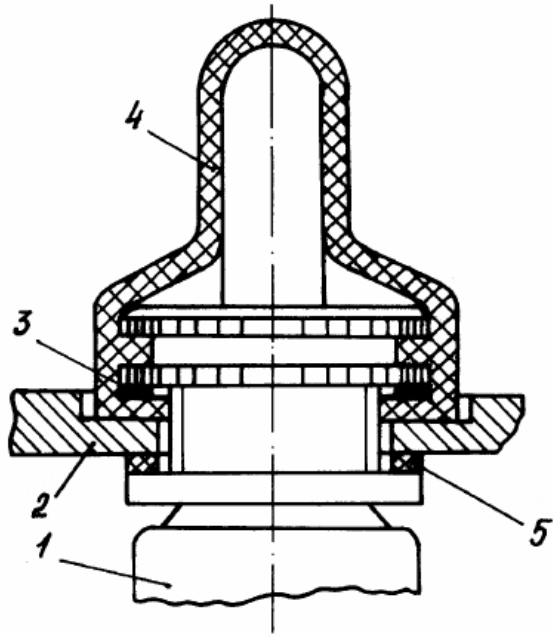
Ущільнення рукоятки тумблера за допомогою гумового ковпачка: 1 – тумблер; 2 – лицьова панель; 3 – металева шайба; 4 – ковпачок; 5 – гумова прокладка
